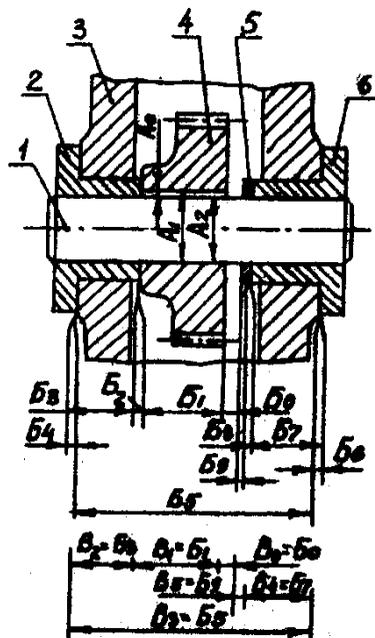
Размерные цепи, обеспечивающие вращение шестерни на оси
